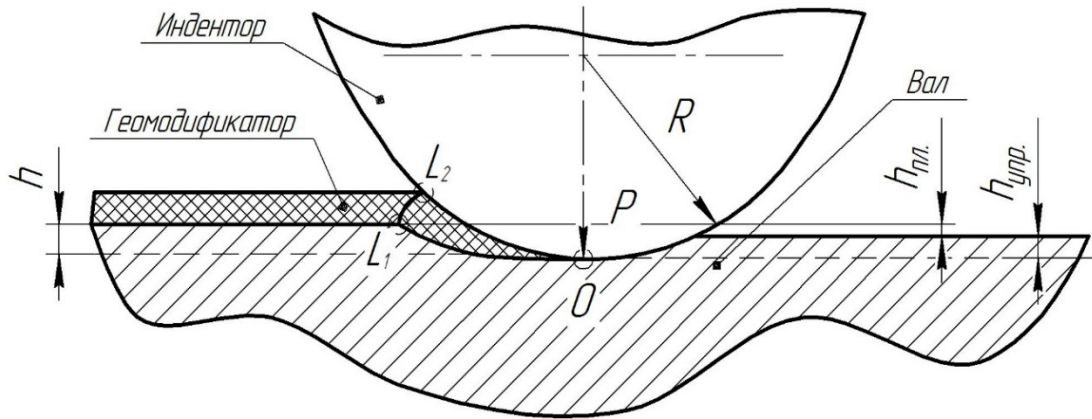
Схема контакта шарового индентора с поверхностью детали при алмазном выглаживании
